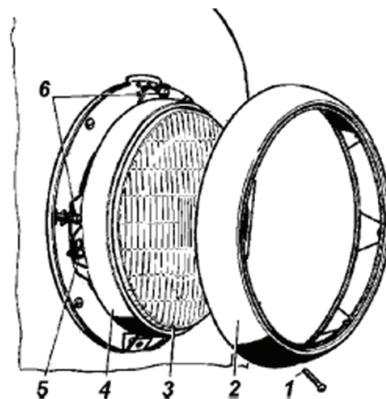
Фара: 1,5 - винты; 2 - декоративный ободок; 3 - оптический элемент; 4 - внутренний ободок; 6 - регулировочные винты
